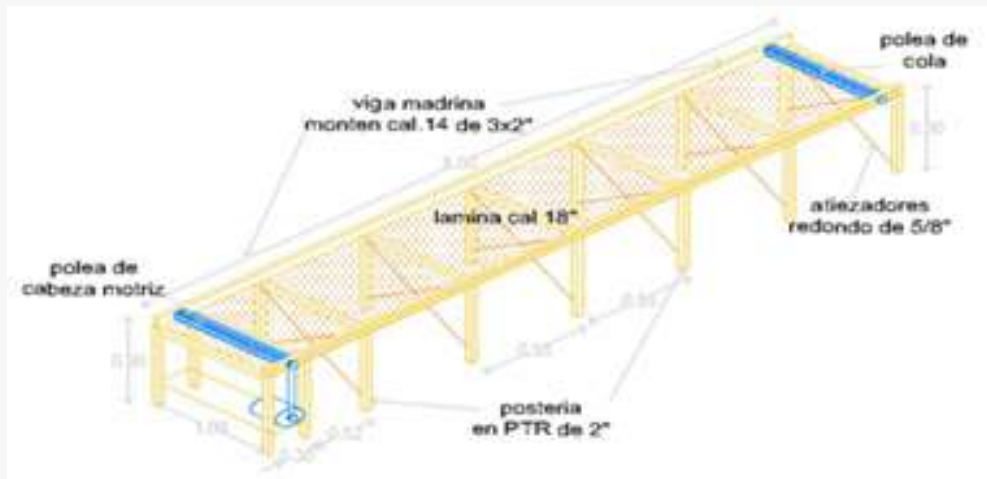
Materiales y accesorios a utilizar en el ensamble del equipo.
